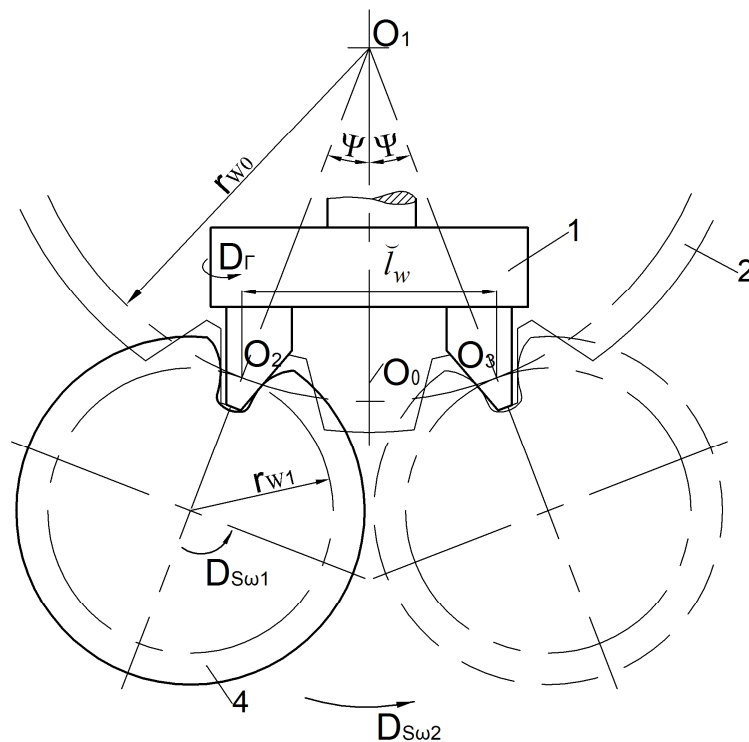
Схема формообразования зубьев цилиндрического колеса
